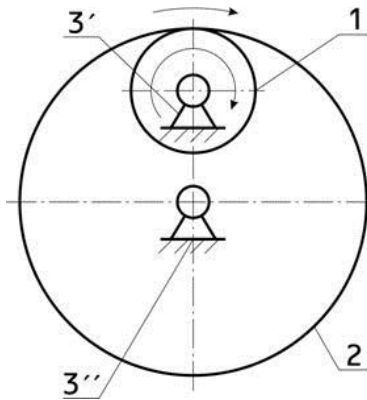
Зубчатый механизм с внутренним зацеплением
